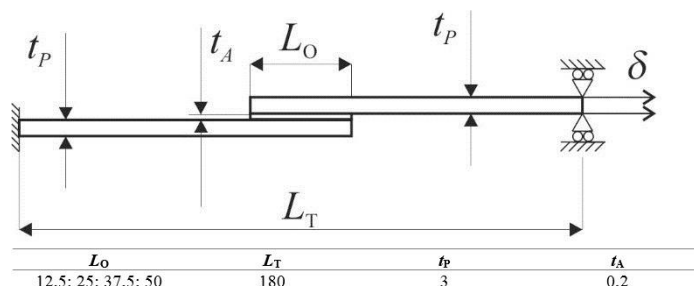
Configuração e dimensões da junta (em mm) [55].
